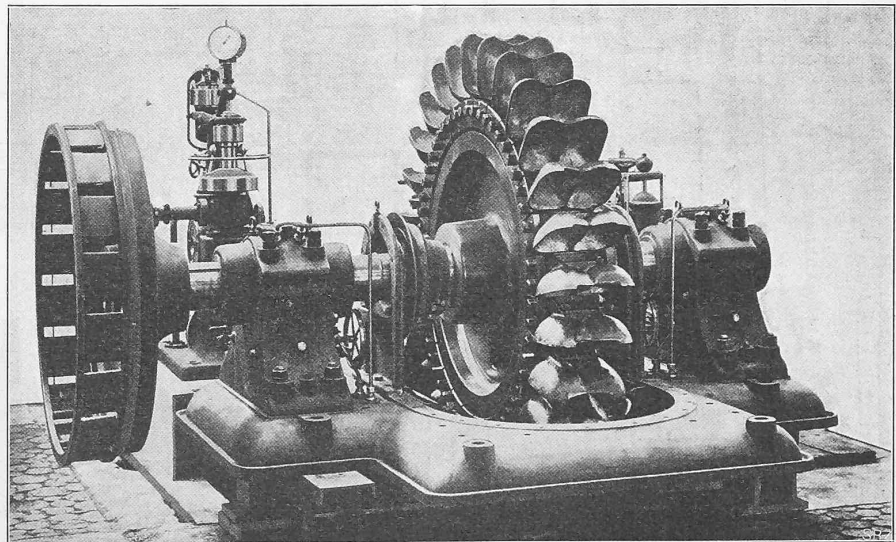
Ansicht der Turbine ohne Gehäuse.
